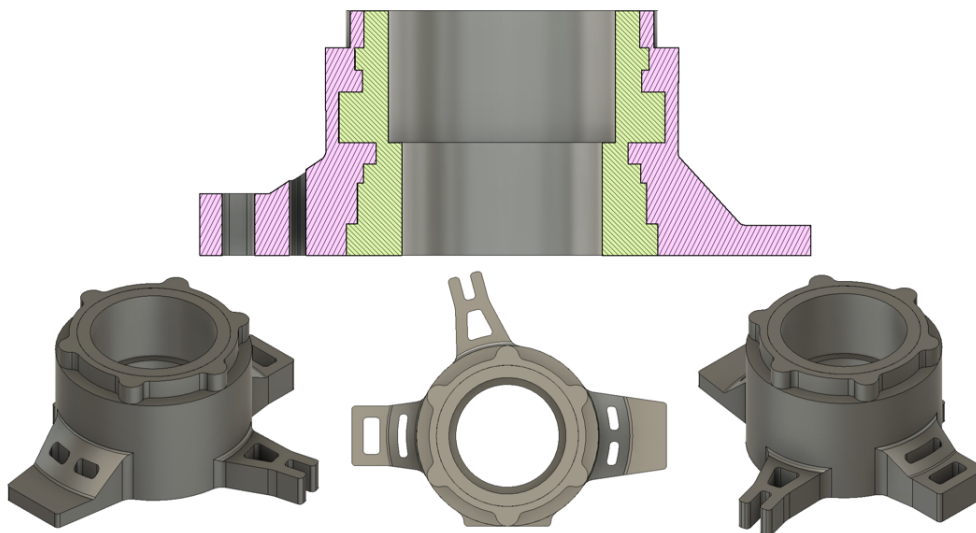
Diseño de la geometría de la preforma a fabricar (Elaboración propia).
